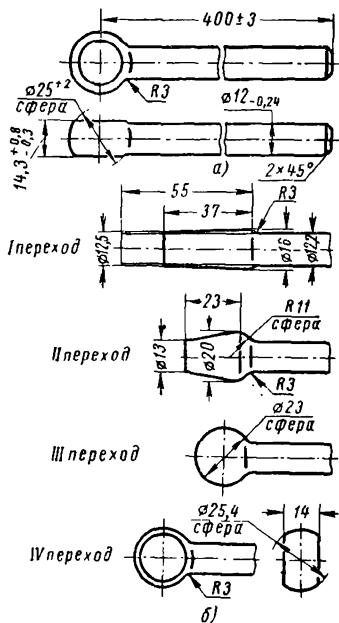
Поковка вида стержня с утолщением: а — поковка; б — переходы штамповки
